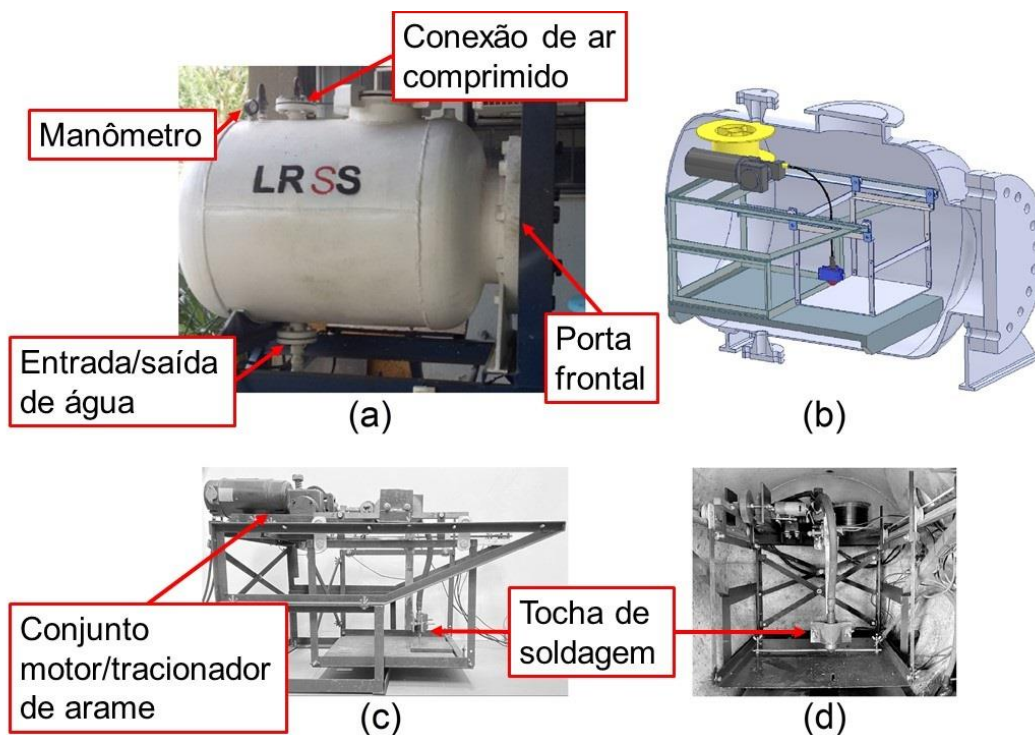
(a) Câmara hiperbárica, (b) projeto tridimensional da máquina de soldagem, (c) vista lateral da máquina e (d) vista frontal da máquina dentro do tanque.
